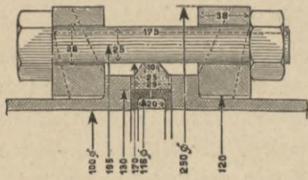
Flanschdichtung der 100 mm im Lichten weiten Druckwasserleitung.
